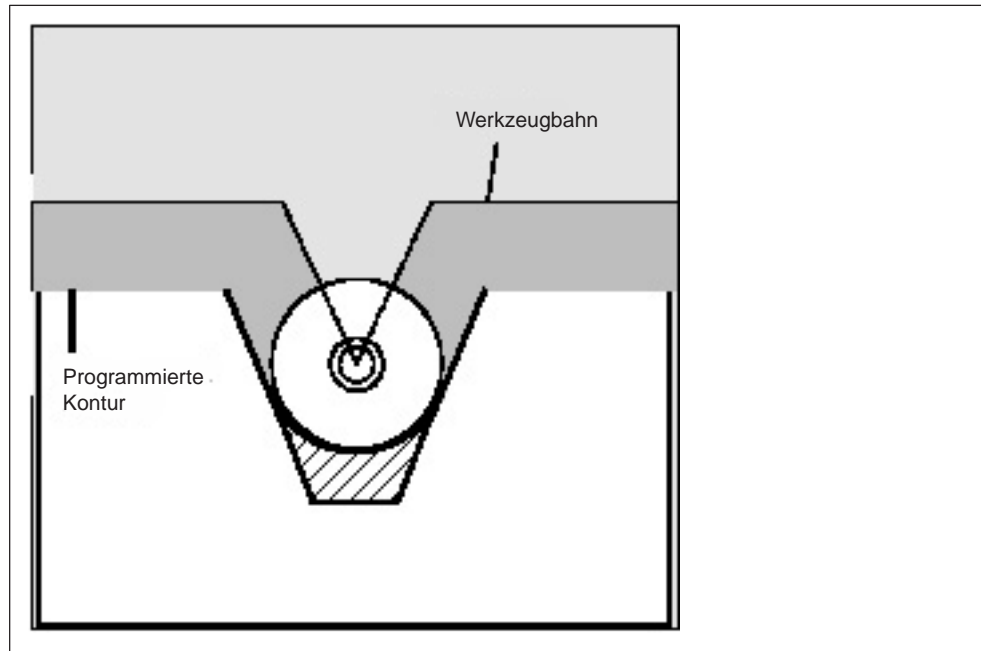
Werkzeugradius zu groß für Innenbearbeitung
